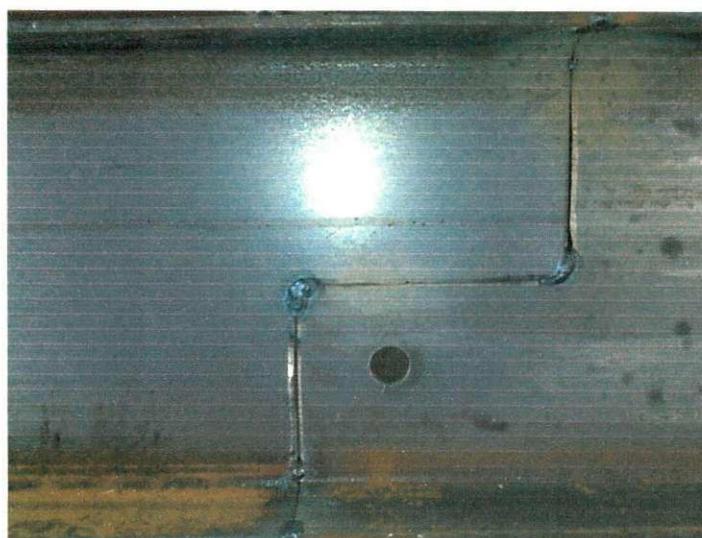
Método de ponteamto utilizado o processo de soldagem MIG/MAG.
